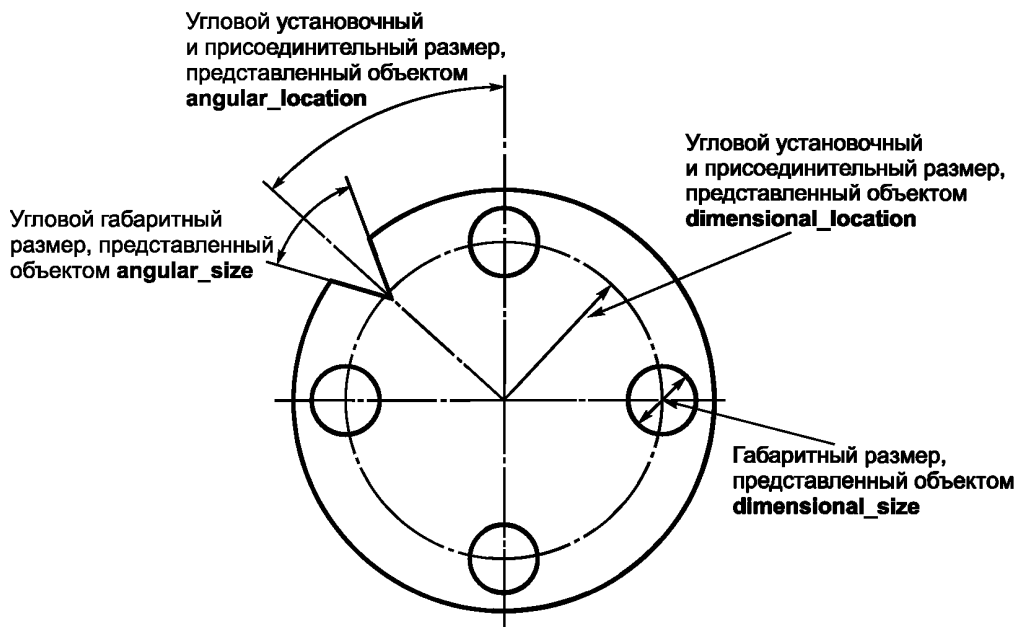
Установочный и присоединительный размер и габаритный размер
